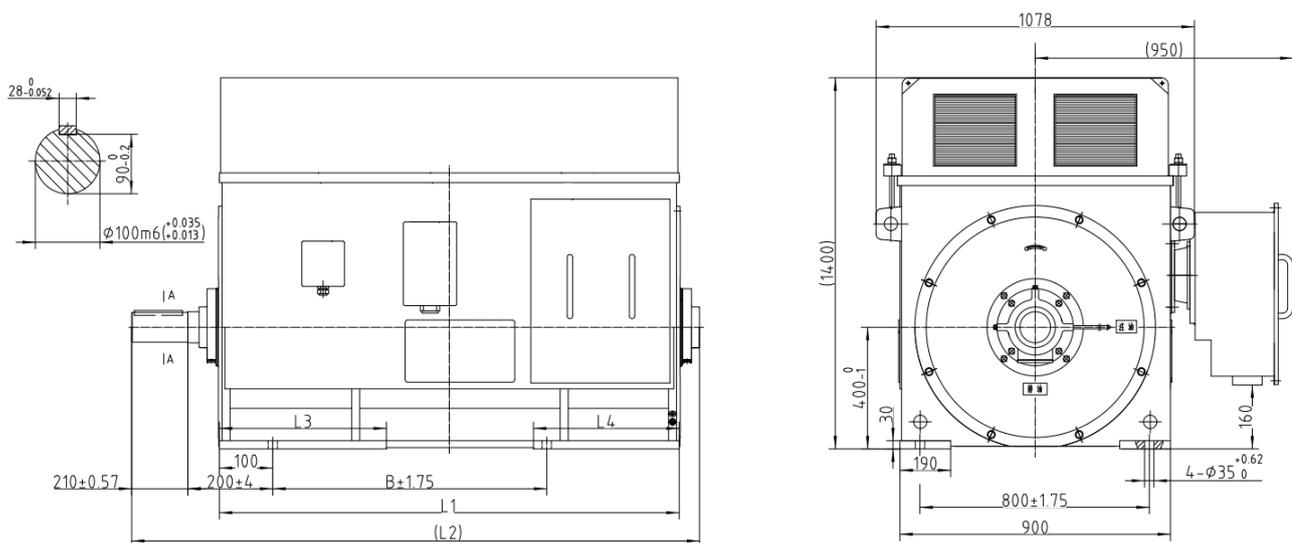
Асинхронные двигатели серии А4-400 6 кВ. Габаритные, установочные и присоединительные размеры.
